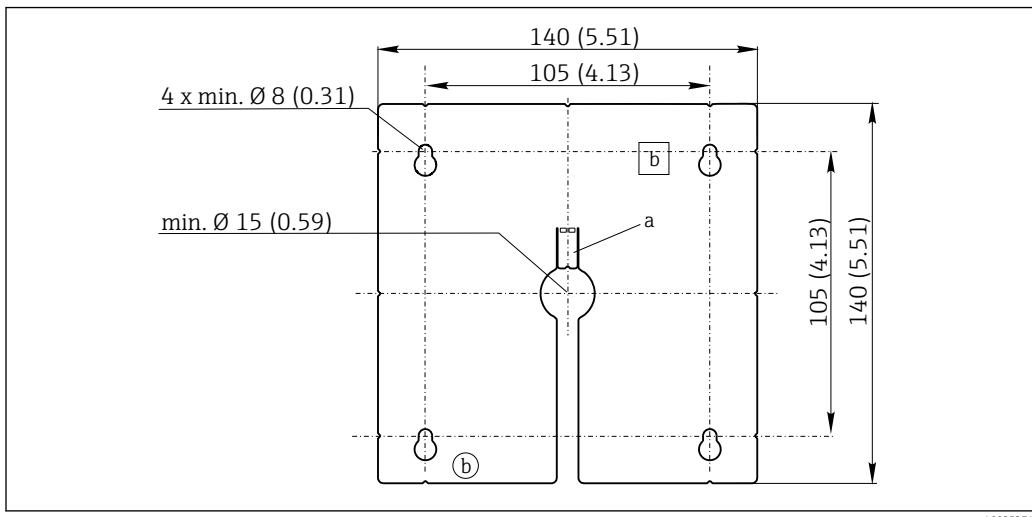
Piastra di montaggio del display separato, dimensioni in mm (in)
